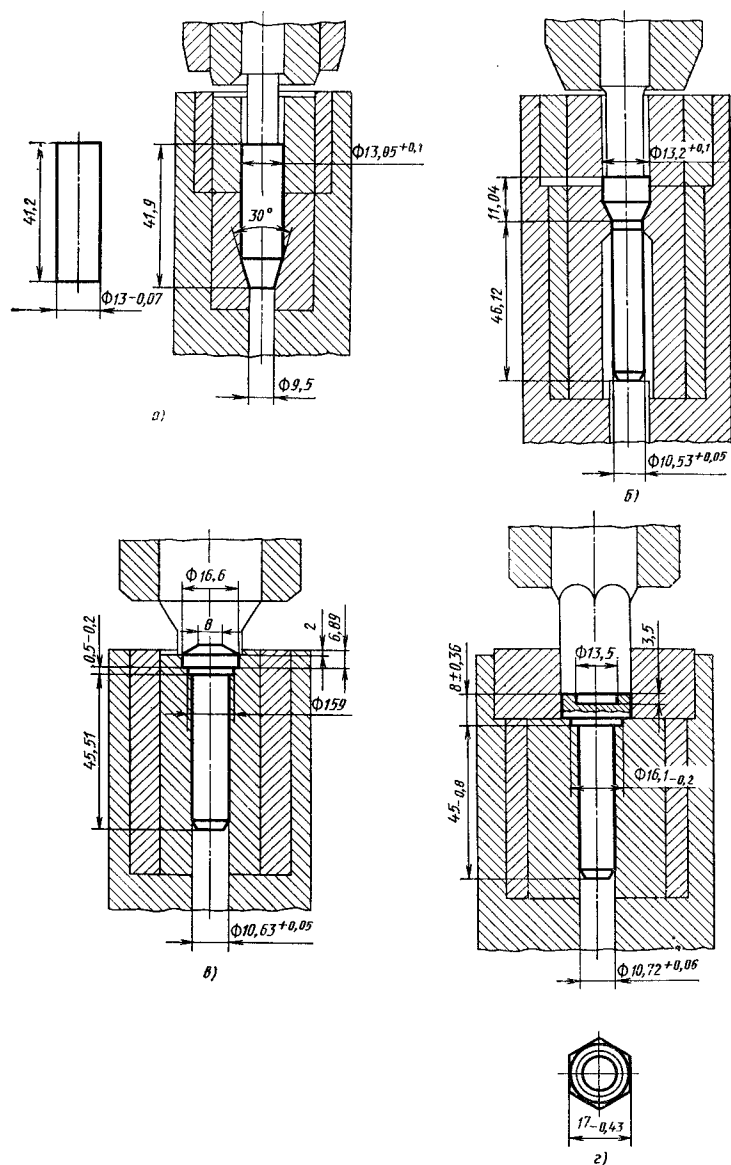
Переходы и наладка рабочего инструмента при штамповке болта с формованием головки:
